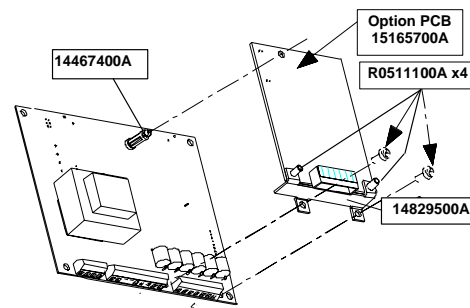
Montando la PCB Modbus Plus opcional en el gabinete de montaje en panel
